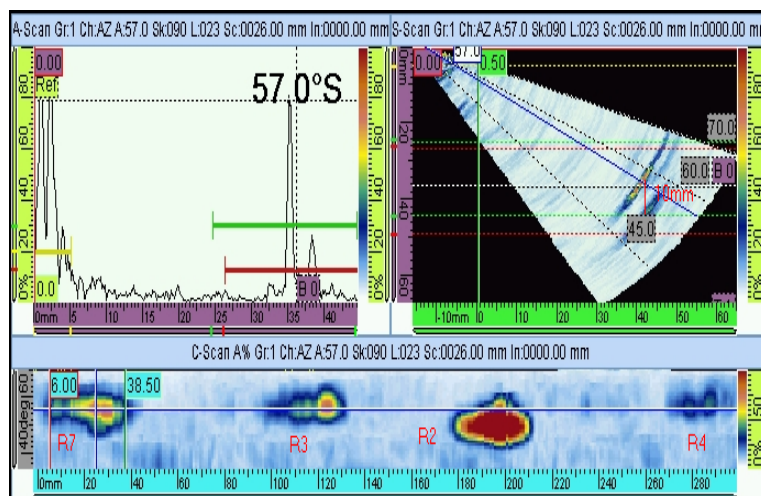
Sou asné zobrazení A - scanu S - scanu a C-scanu p i zkoušení svaru.
